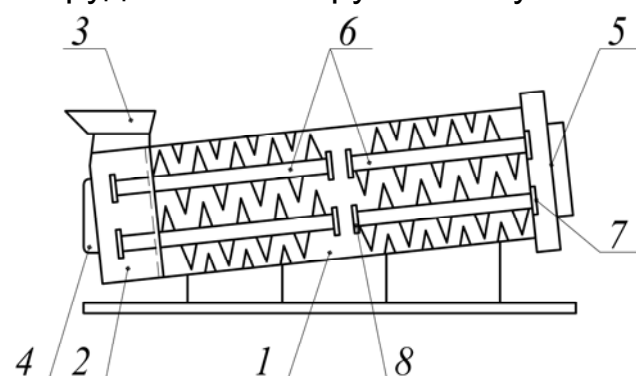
Схема пошкодженого дифузійного апарата типу ПДС-20: 1 – корпус; 2 – камера; 3 – шахта; 4,5 – нижній та верхній приводи; 6 – шнек; 7,8 – зовнішня та внутрішня підшипникові опори
